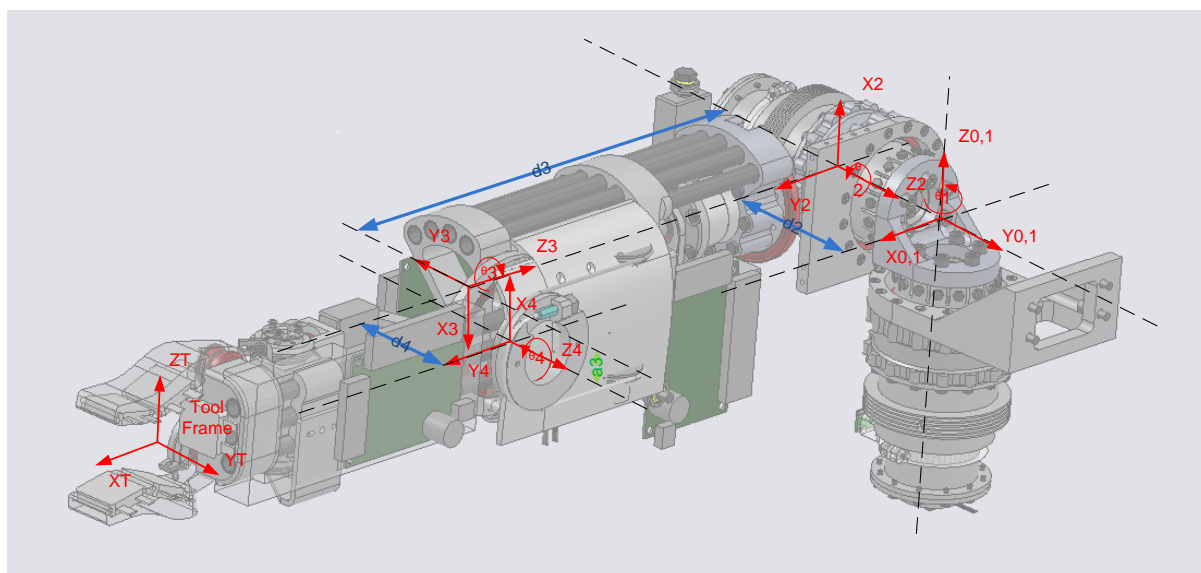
PLACEMENT DES REPERES DU BRAS DROIT
